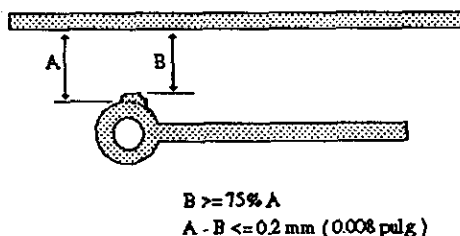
Protección de la mascarilla de soldado (solder mask).
